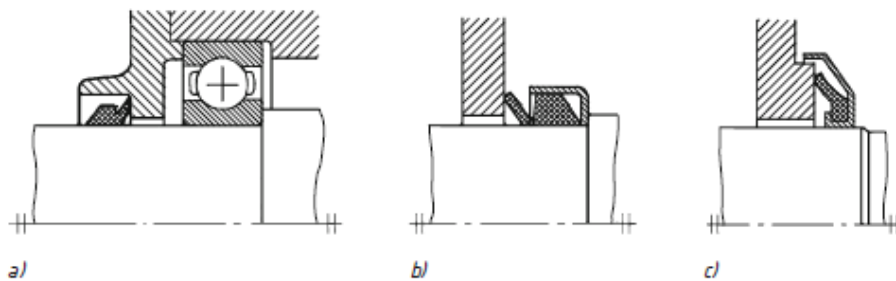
V-Ringe. a) Grundform, b) mit Haltering, c) Gamma-Ring
